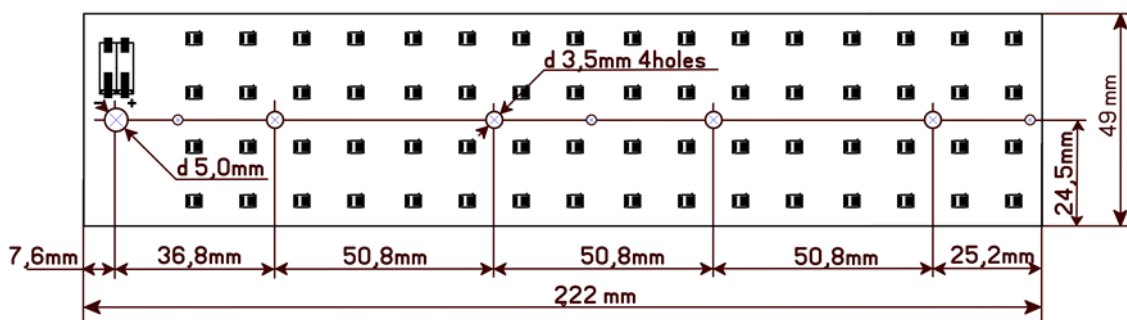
Габаритные размеры светодиодного модуля ALC222.49.64-х-LM301D-XXXX
